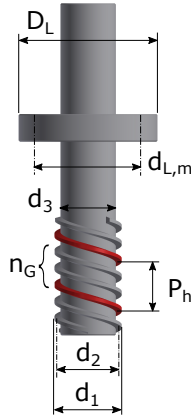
Abmessungen der Gewindespindel mit Gleitlager.
